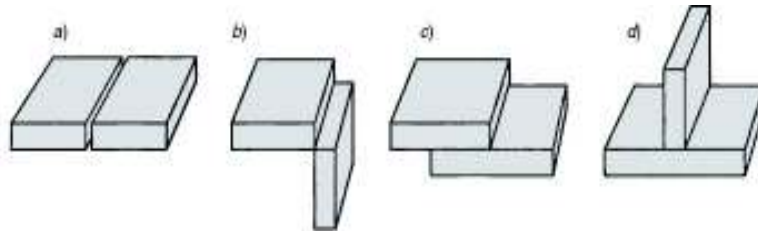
Tipos de juntas soldadas: a) a tope, (b) de esquina, (c), de traslape y (d) en T.
